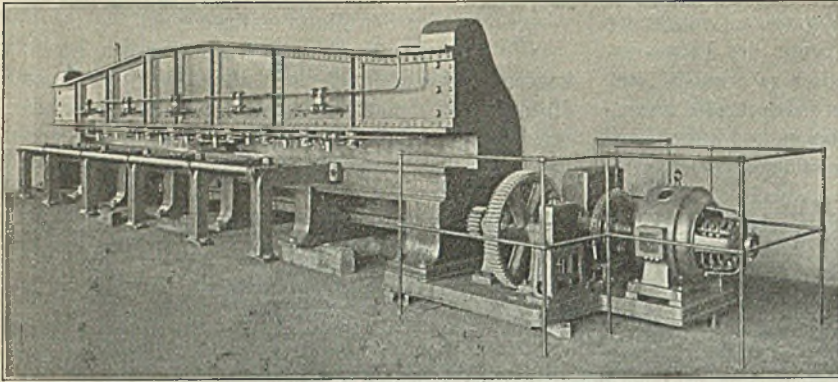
Blechkanten-Hobelmaschine der Dampfkessel- und Gasometerfabrik A. G., vorm. A. Wilke, Braunschweig.
